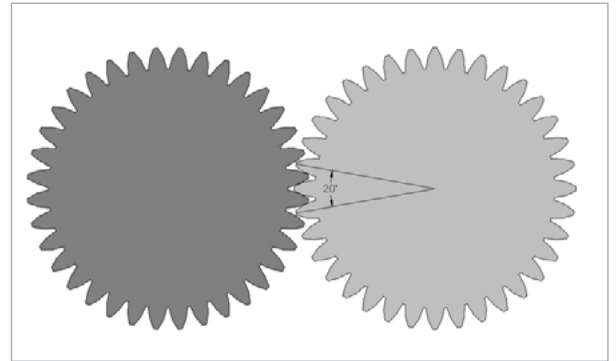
일반적인 치차열의 치형접촉률 [Figure 3. Teeth Engagement in Conventional Gear Train]
